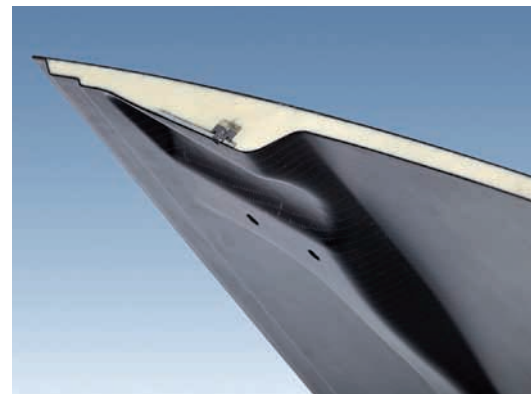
Поперечное сечение модуля для откидного верха автомобиля
